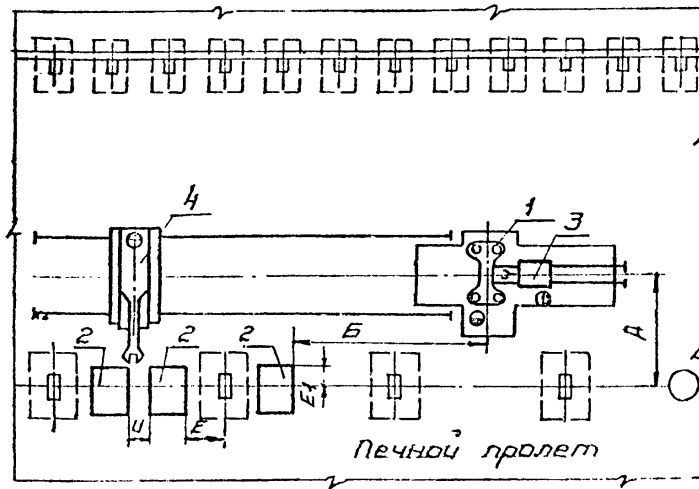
Схема расположения участка гидравлических ковочных прессов усилием 8000-12500 кН:
